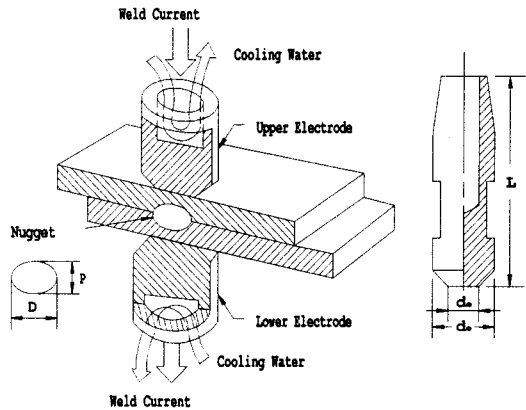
Schematic Diagram of Resistance Spot Welding
